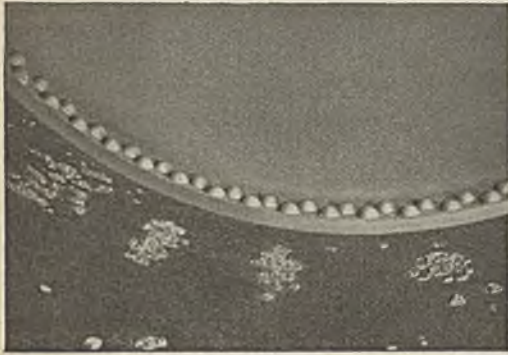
Aufgetragenes Schweißgut auf angefressenen Stellen in einem Dampfkessel.
